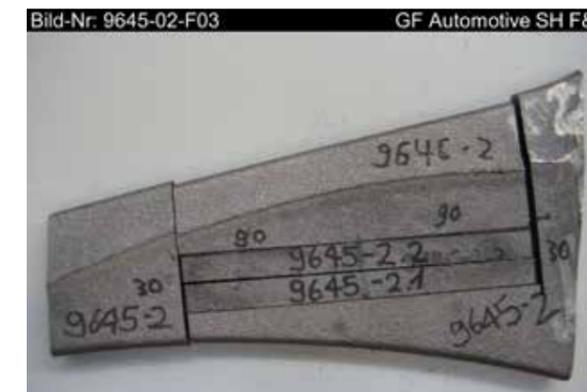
, 1b: Dem Bauteil wurden Proben für Biegeversuche statisch und dynamisch unter schlagartiger Beanspruchung entnommen. Dimensionen der Proben: Wanddicke 14.8 bis 17.5 mm, Breite auf 12.1 mm geschliffen, Länge 180 mm. Wichtig: Der Rissausgangsbereich bei der Prüfung ist die unbearbeitete Gusshaut.
